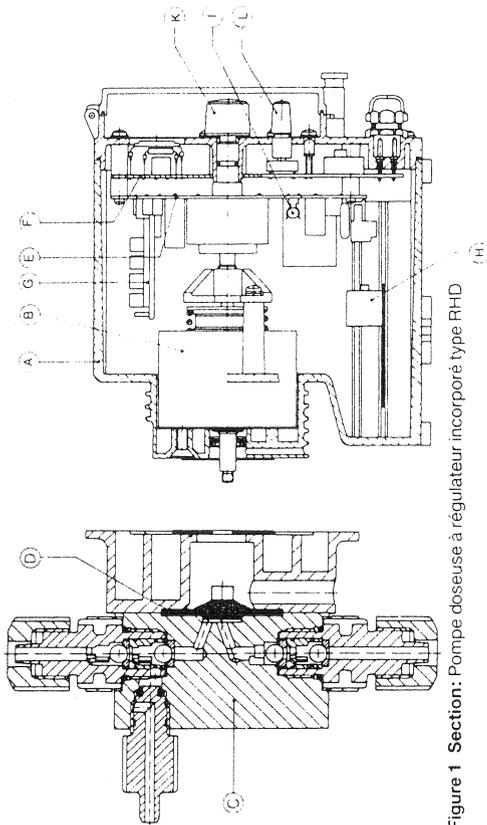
Section: Pompe doseuse à régulateur incorporé type RHD
